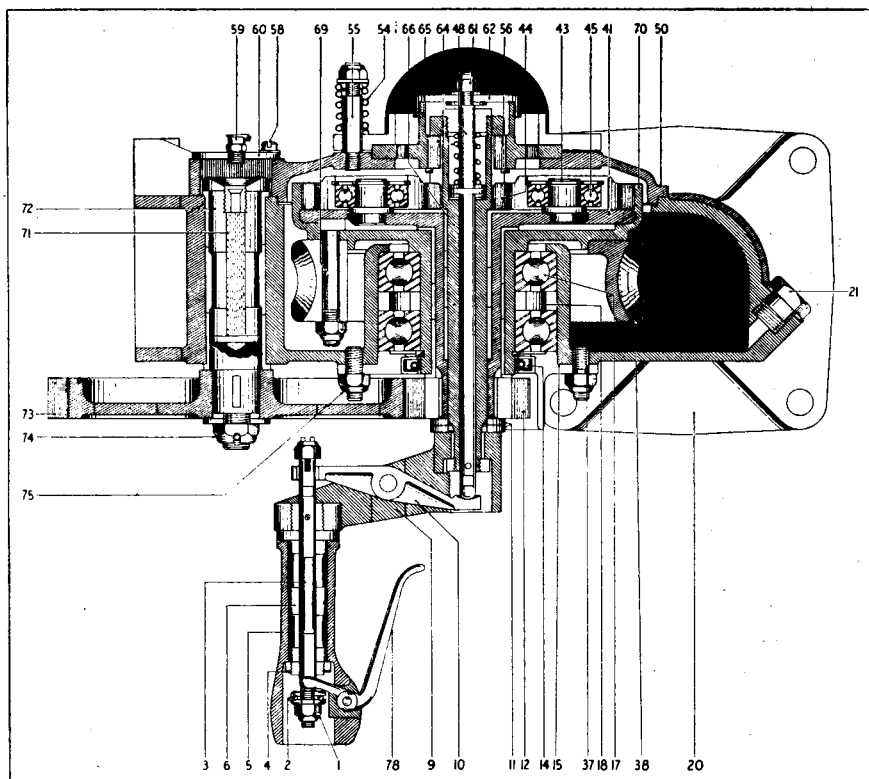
Разрез редуктора (коробки передач) механизма поворота башни (ручной привод и электропривод).
